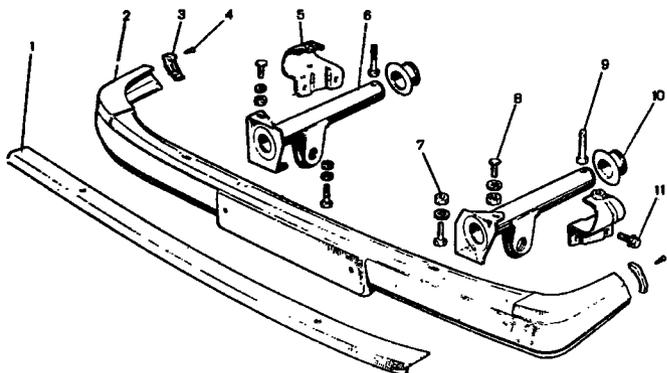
Передний бампер: 1 - накладка; 2 - бампер; 3 - заглушка бампера; 4 - винт крепления заглушек; 5 - внутренний кронштейн; 6 - соединитель бампера с передним кронштейном; 7 - болт крепления бампера; 8 - болт крепления накладки; 9 - болт крепления соединителя к внутреннему кронштейну; 10 - резиновый уплотнитель; 11 - болт крепления внутреннего кронштейна к кузову
